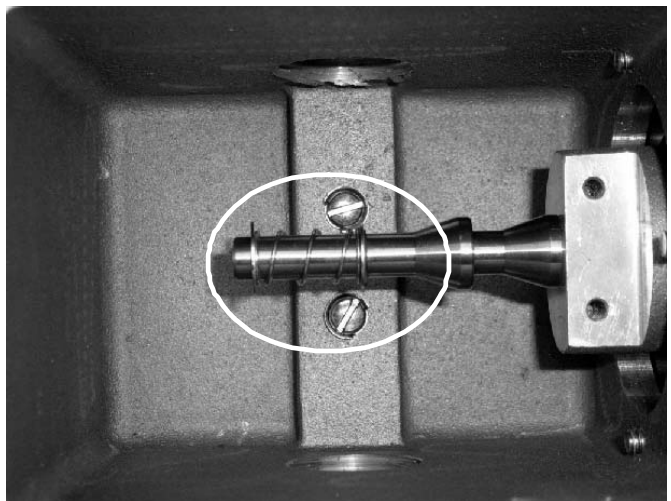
Use a mão para segurar o retentor de mola, enquanto remove os parafusos. Não remova a mola e as arruelas do eixo. Nos interruptores DPDT, use um alicate de crimpagem 0640014100 ou de cabeça de crimpagem 0640054100 com a ferramenta pneumática manual AT-200, para prender os conectores bandeira isolados aos fios.
